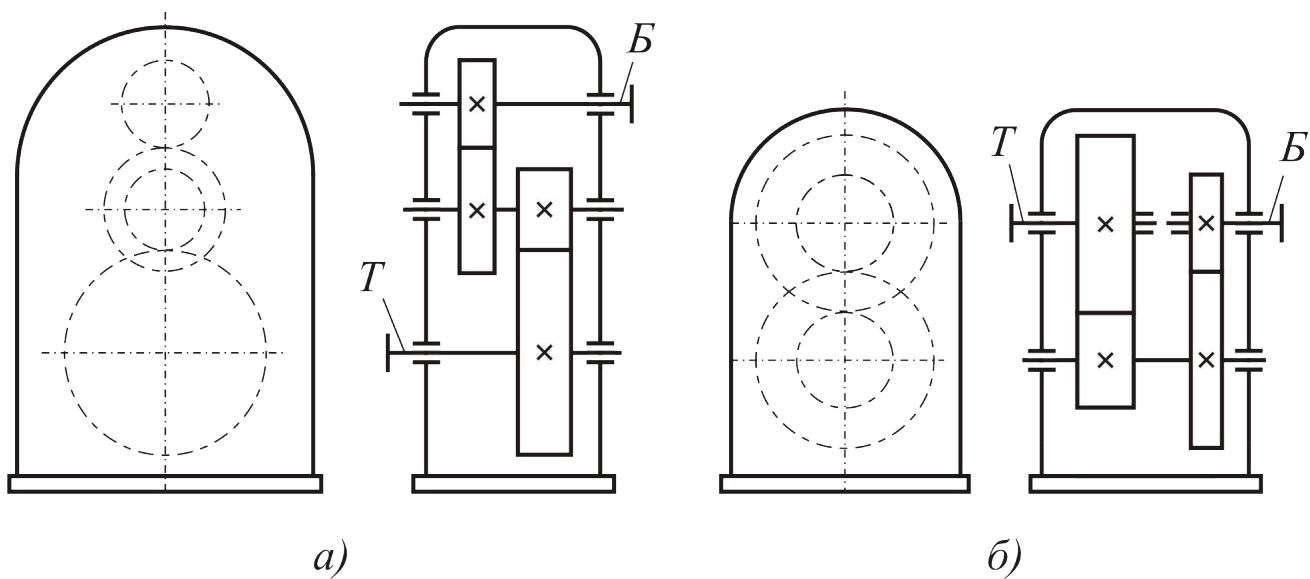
Кинематические схемы двухступенчатых цилиндрических вертикальных редукторов: а) развёрнутая схема; б) соосная схема
